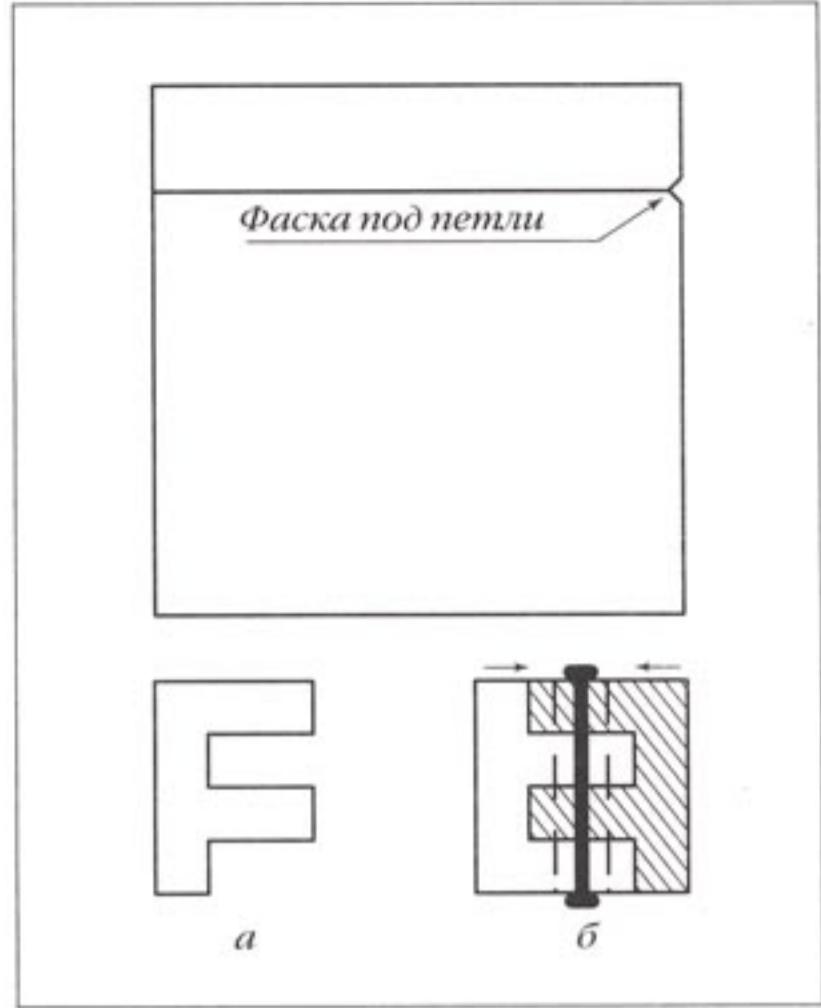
Изготовление петли: а – половинка петли; б –стыковка половинок петель
